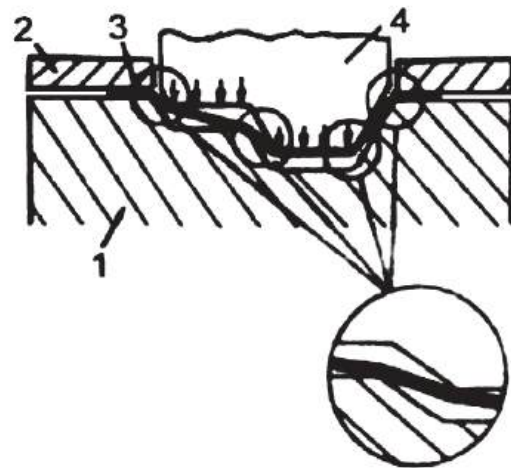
Схема формозміни листової деталі складної форми:
